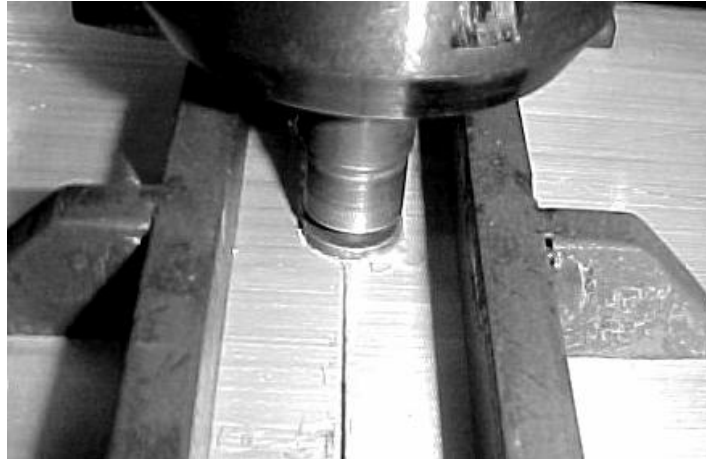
Vista general de un equipo utilizado para la Soldadura por Fricción y Agitación
